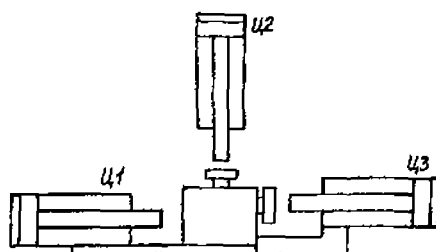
Конструктивная схема запрессовочного приспособления
